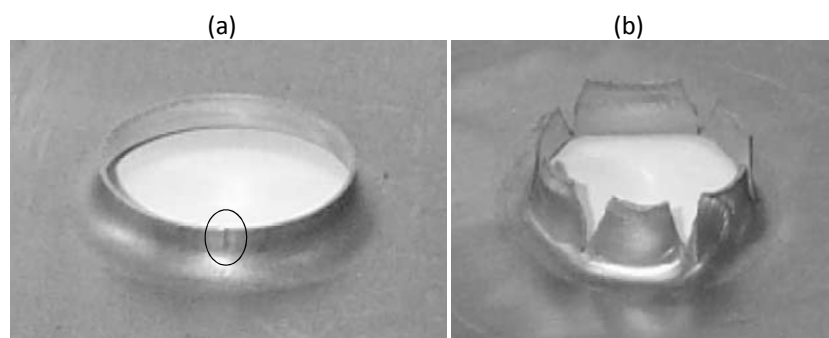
Exemples de défauts : (a) strictions (b) déchirures axiales [23]
